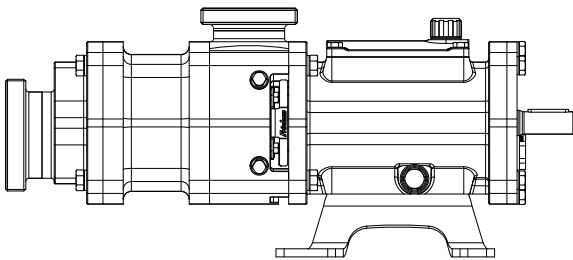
Máquina incompleta: bomba sin motor, acoplamiento y bastidor
